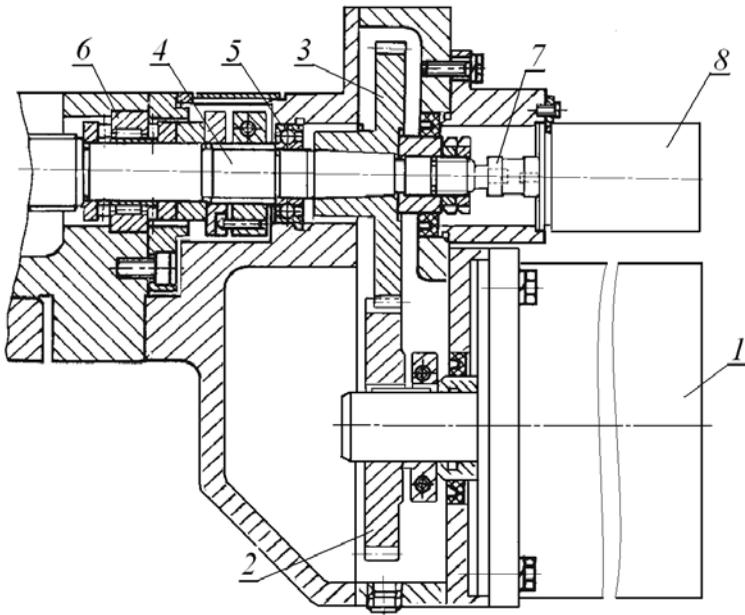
Привод поперечной подачи суппорта токарного станка с ЧПУ модели 16К20Ф3
